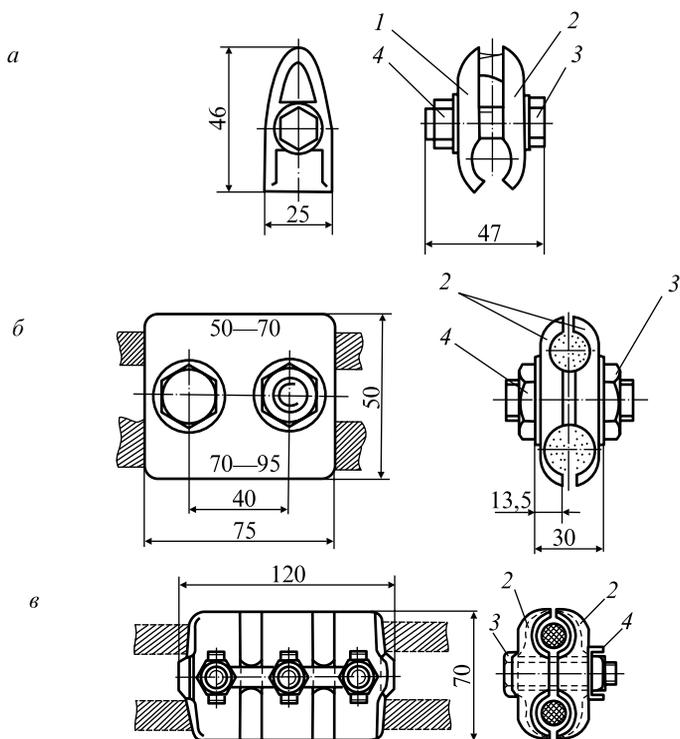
Арматура из цветного литья: *а* — зажим струновой 046; *б* — зажим соединительный 054; *в* — зажим соединительный для алюминиевых проводов; 1 — щека с резьбой; 2 — щека без резьбы; 3 — болт М12; 4 — гайка М12
